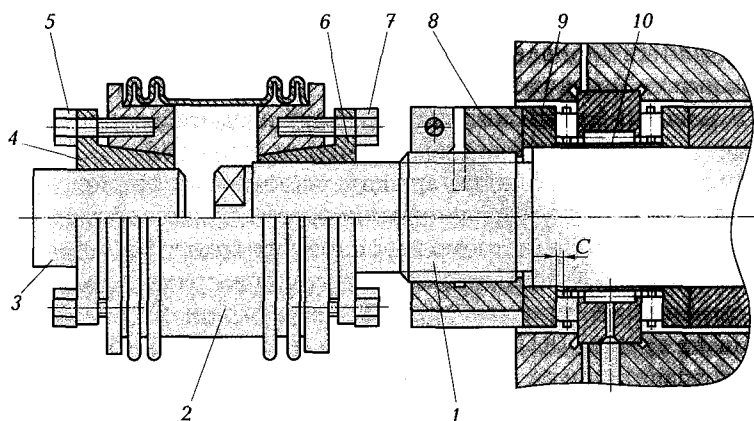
Конструкция соединительной муфты и опоры ходового винта:
